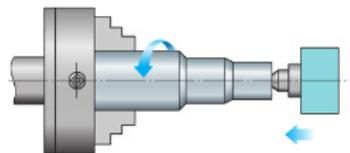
Закрепление заготовки в патроне с подвижным задним центром
